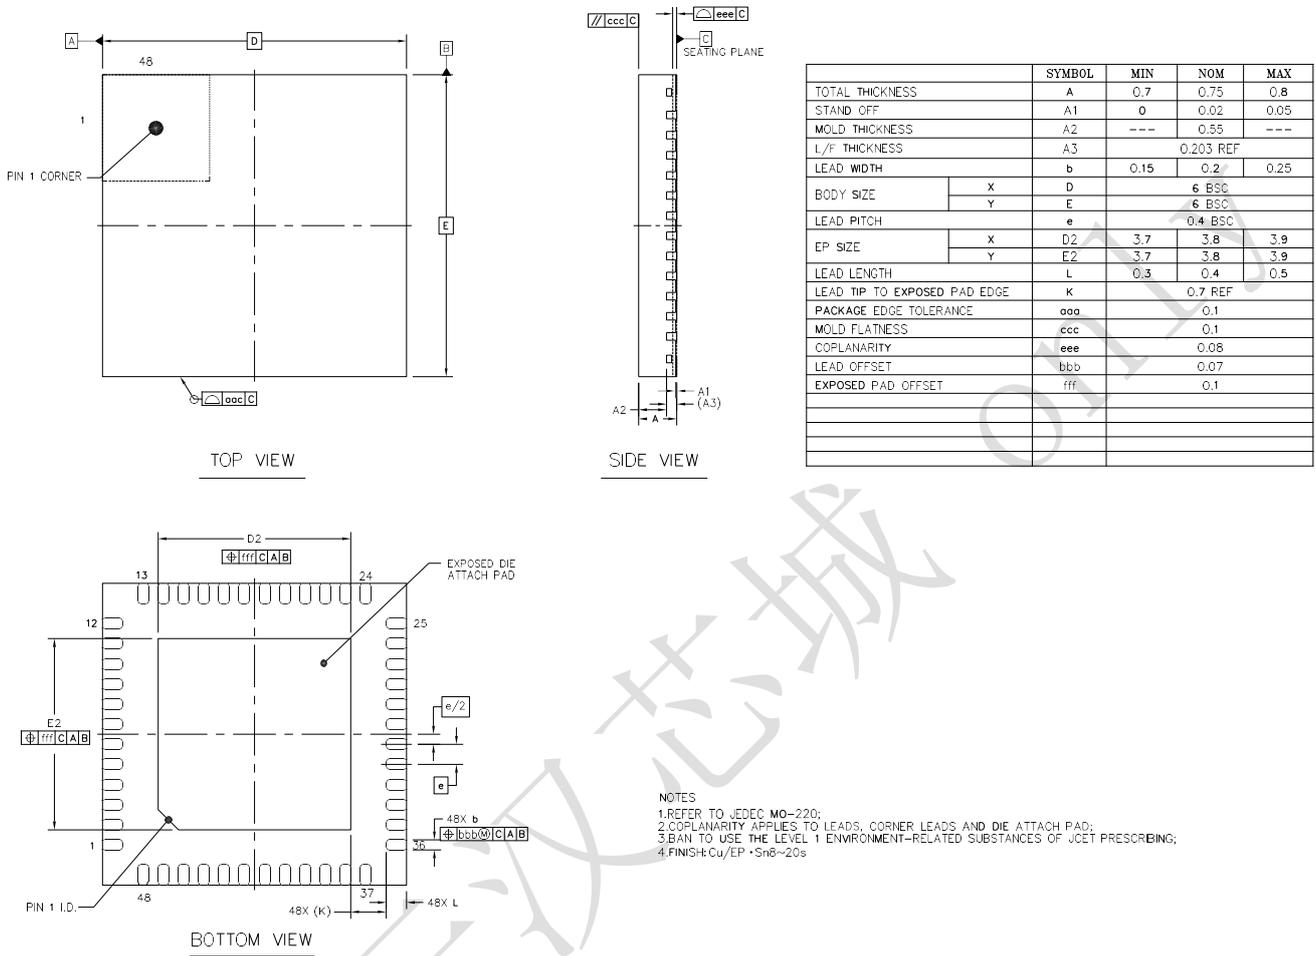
FR8023D / FR8028D / FR8028DP 封装尺寸图
